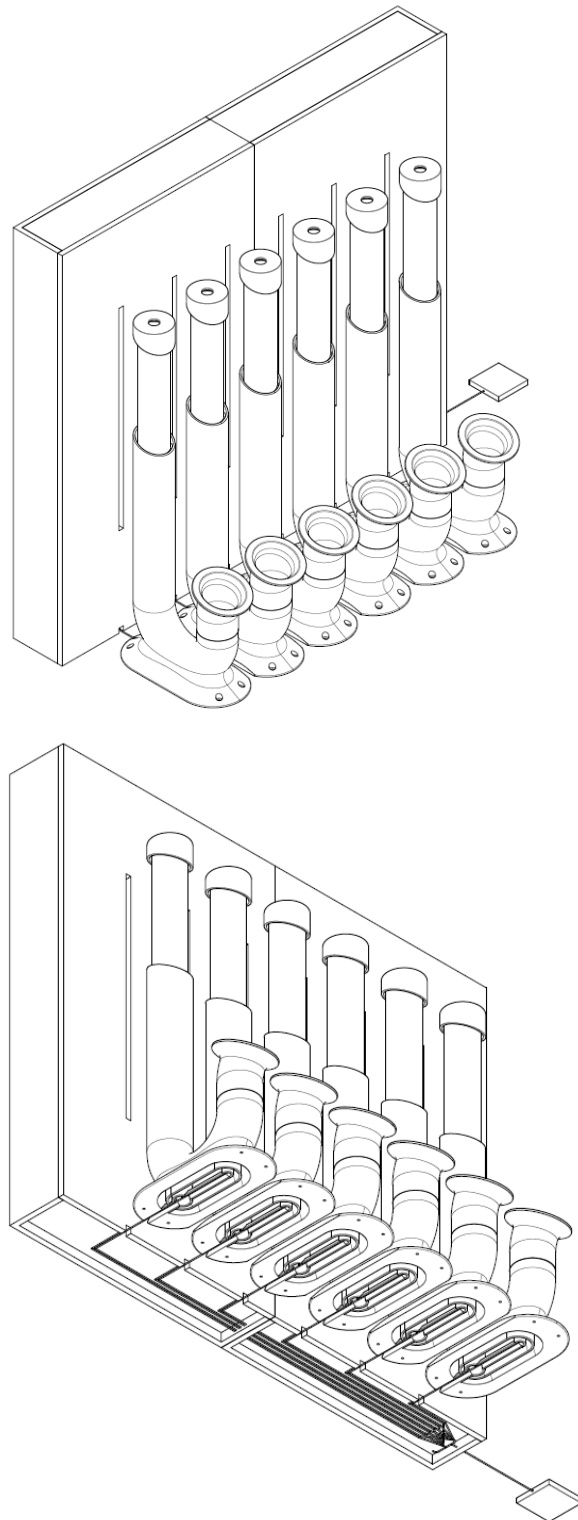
e 160 – Vistas isométricas do Conjunto Completo.
